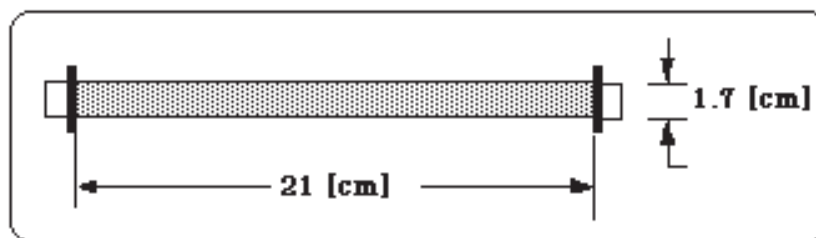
Dibujo de una bobina con sus actuales dimensiones.
